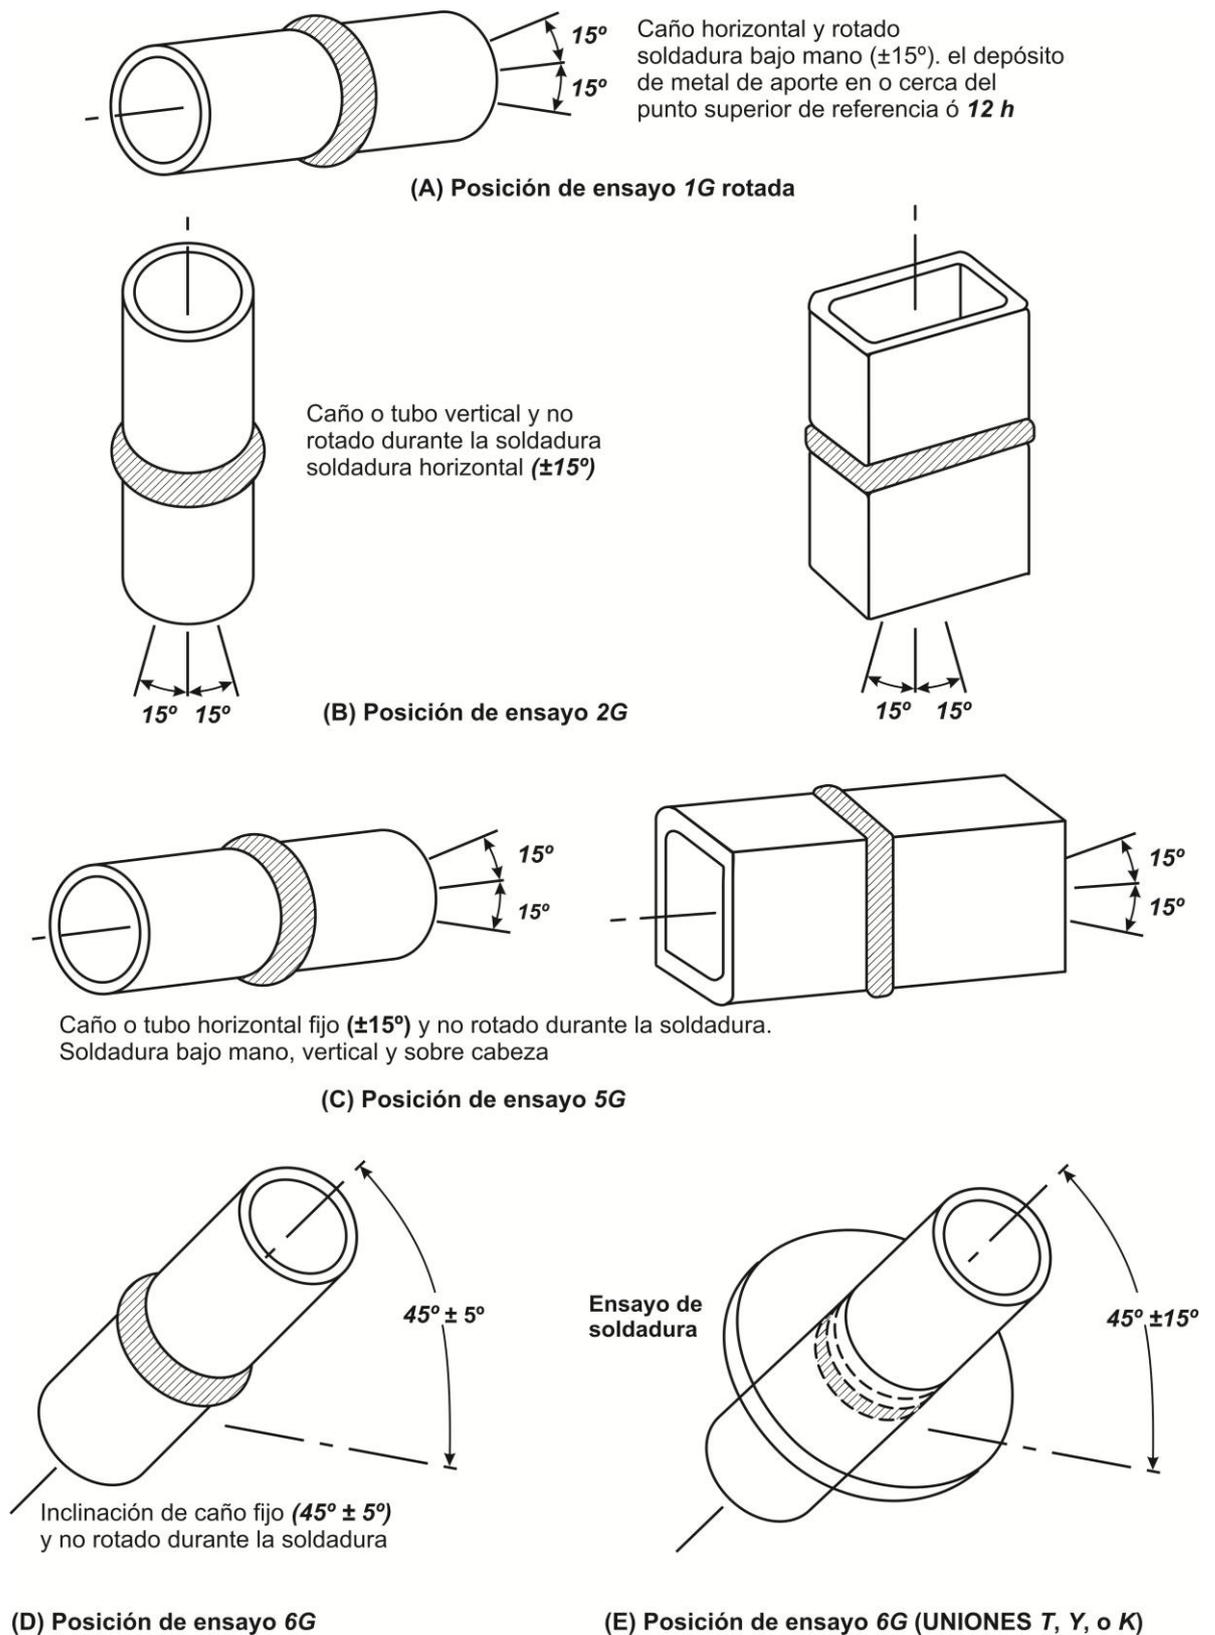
Posiciones de ensayo de caño o tubo para soldaduras con bisel.
